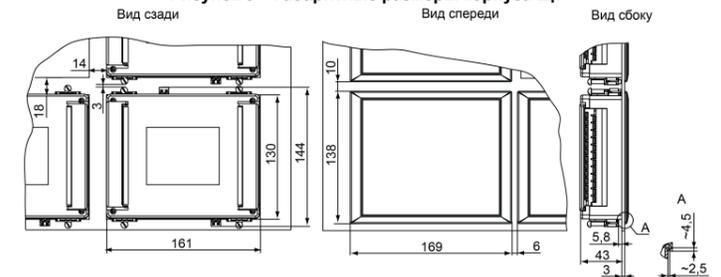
Прибор в корпусе Щ7, установленный в щит толщиной 3 мм
